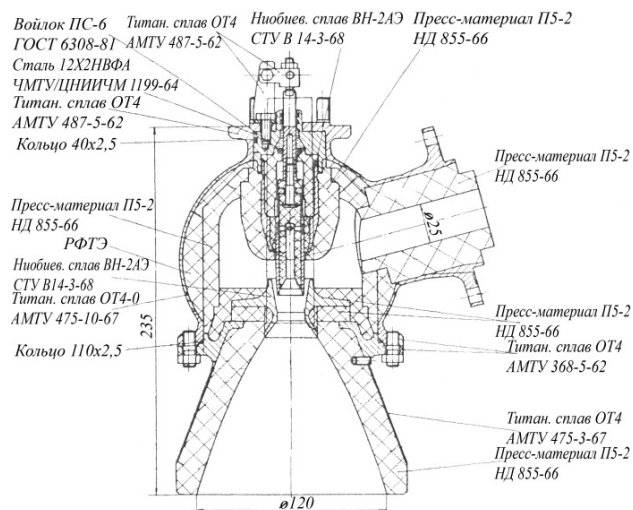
Конструкция управляющего сопла двигателя 15Д191
